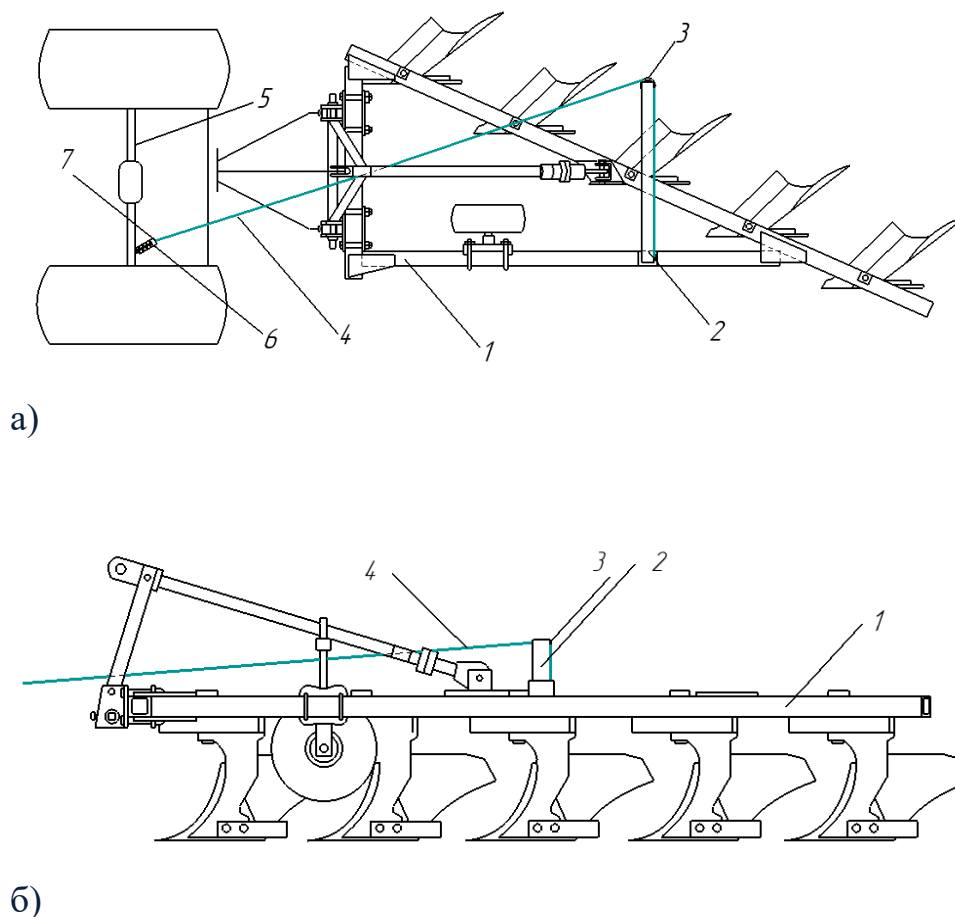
Автоматический корректор–регулятор для стабилизации прямолинейного движения пахотного агрегата:
